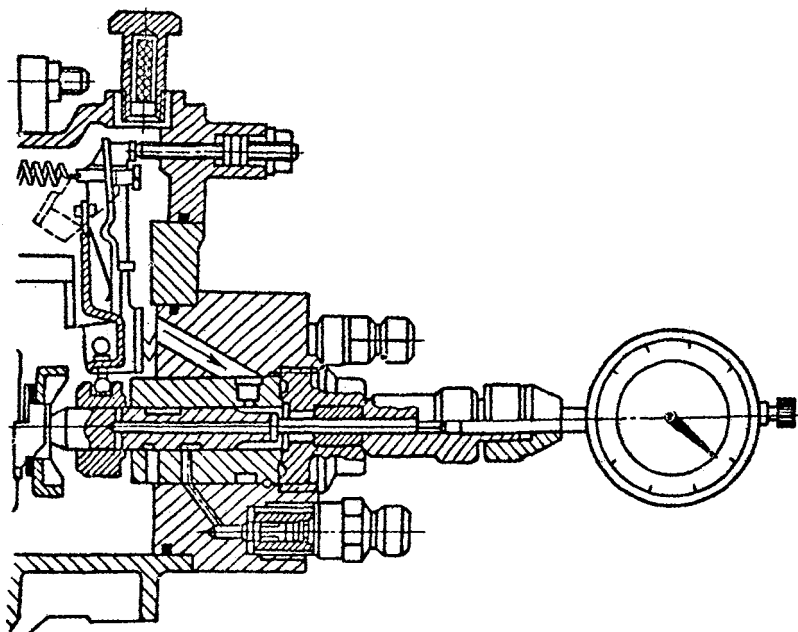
Установка индикатора для проверки момента начала впрыска
